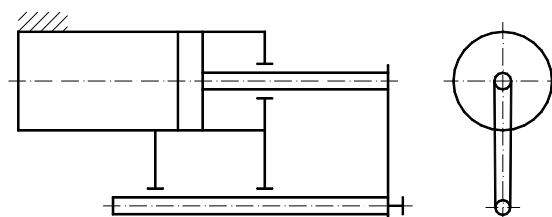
Řešení posuvné PJ se základním a předním posuvným vedením vyhovující tuhosti. V obou případech lze užít principu inverze a nepohyblivým prvkem mohou být vodicí tyče s přírubou, zatímco pohybovat se bude těleso motoru zabudované do saní i když je to méně frekventovaný případ.
